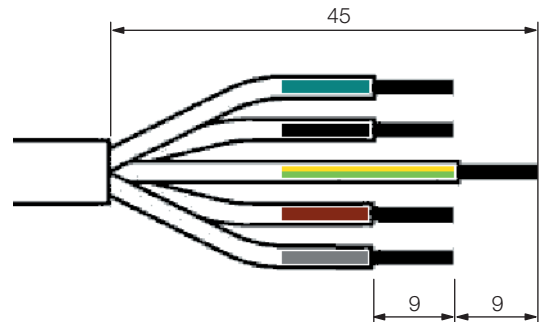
Maße zum Entfernen der Gummiummantelung und der Isolierung
